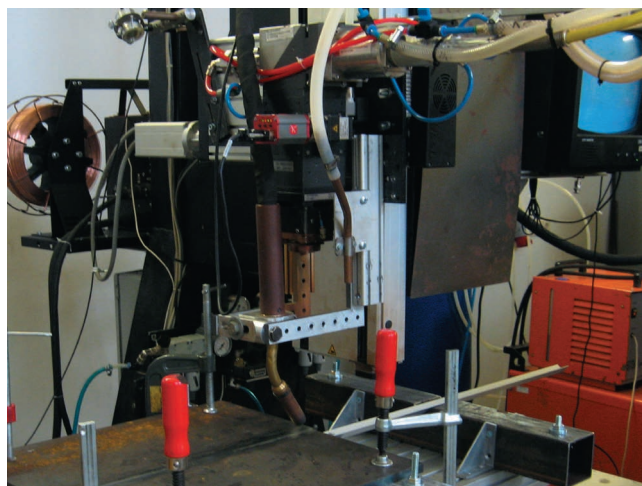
Технологическая установка для лазерно-дуговой сварки металлов больших толщин.
